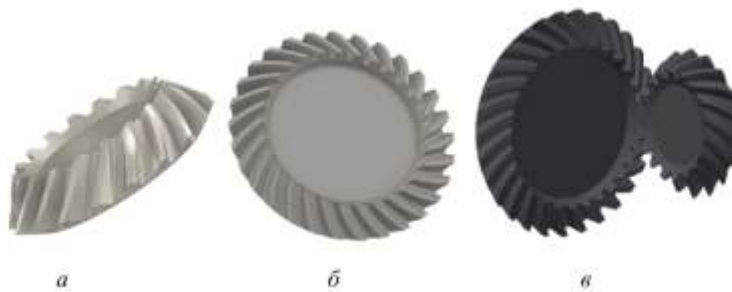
3D-моделі конічної шестерні (а), конічного зубчастого колеса (б) і конічного зубчастого зачеплення (в) [8]
